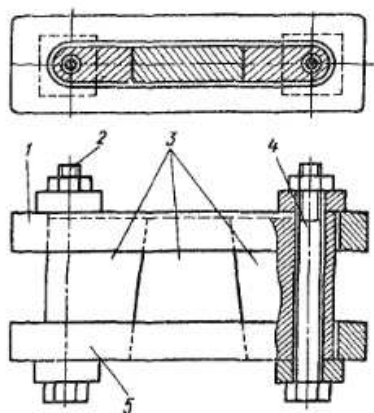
Шаблон для правки и опрессовки катушек, намотанных из шинной меди на ребро
